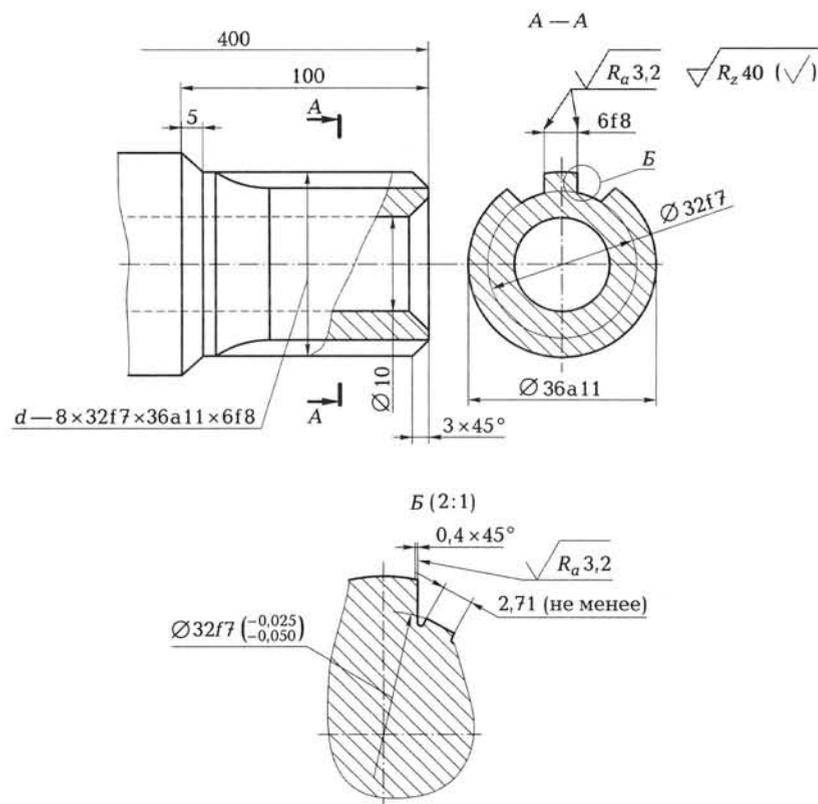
Обозначение на чертеже полей допусков шлицевого вала прямого шлицевого соединения
